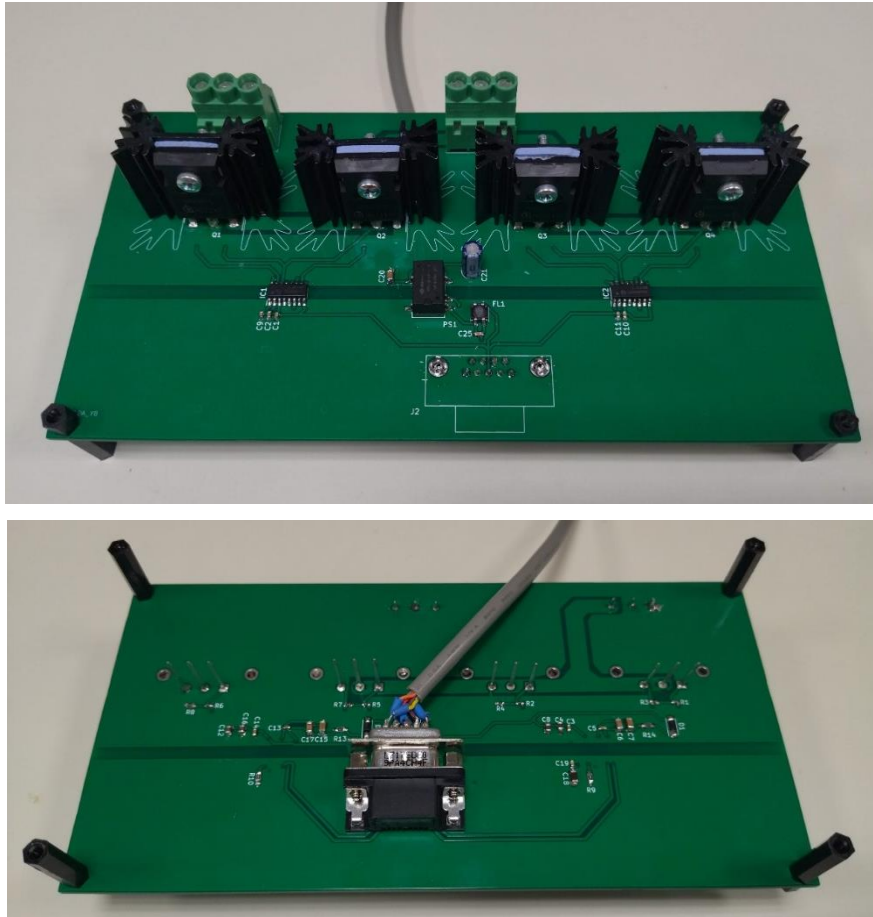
Lado Top y Bottom de la PCB de potencia componentes soldados.
